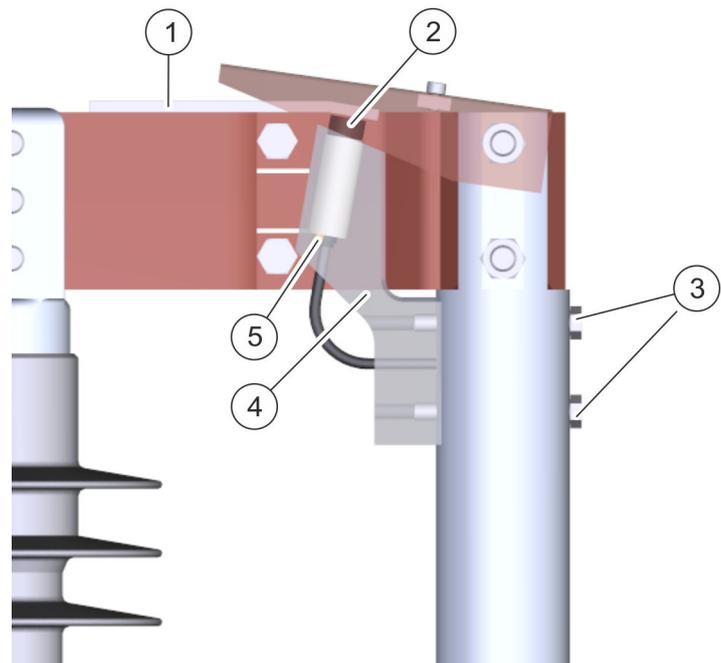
Draufsicht auf die geschlossenen Hauptkontakte, ohne Abdeckblech
